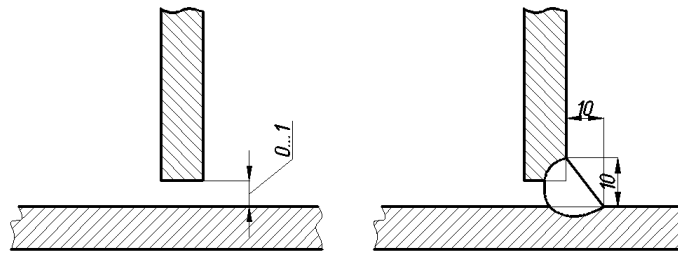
Тип сварного соединения Т1 по ГОСТ 5264-80
